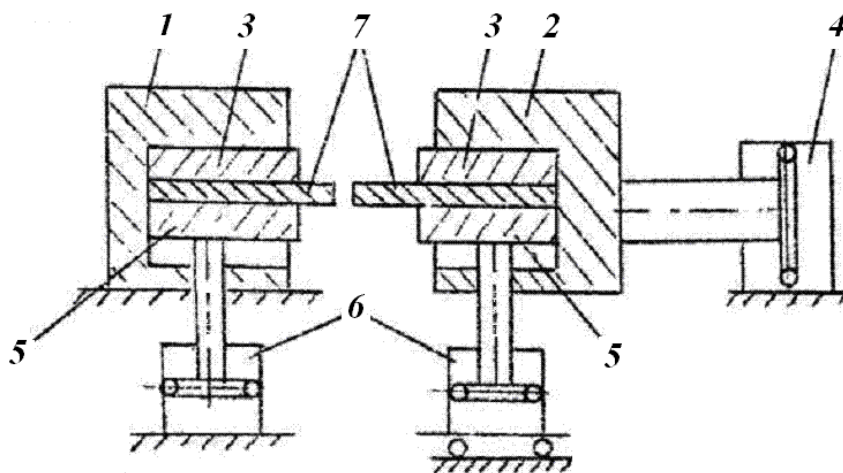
Принципиальная кинематическая схема машины для стыковой сварки: 1 – неподвижная плита; 2 – подвижная плита; 3 – сменная зажимная губка неподвижная; 4 – механизм осадки с цилиндром силового привода; 5 – сменная зажимная губка подвижная; 6 – механизм зажатия с цилиндрами привода; 7 – свариваемые детали
